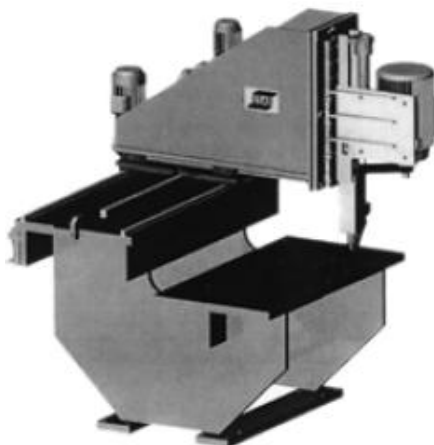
Установка для сварки трением с перемешиванием
